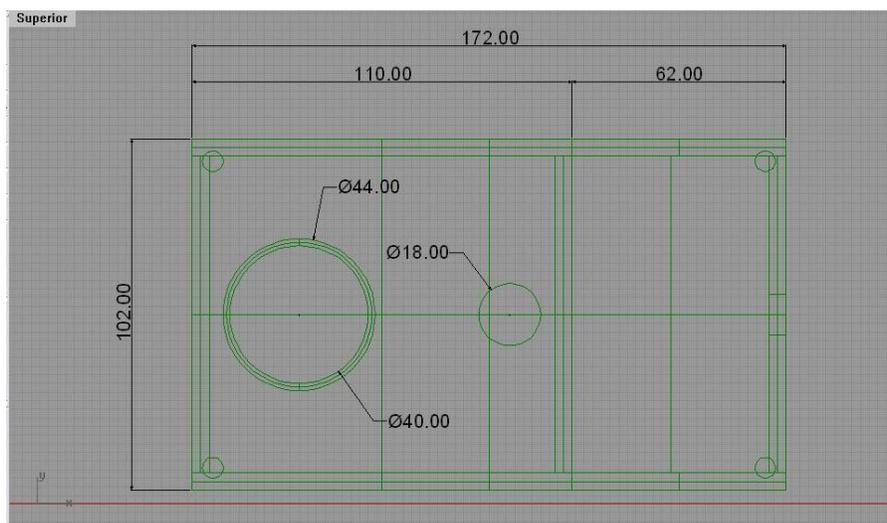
Vista superior del sistema de aislamiento 1:1 en mm.
